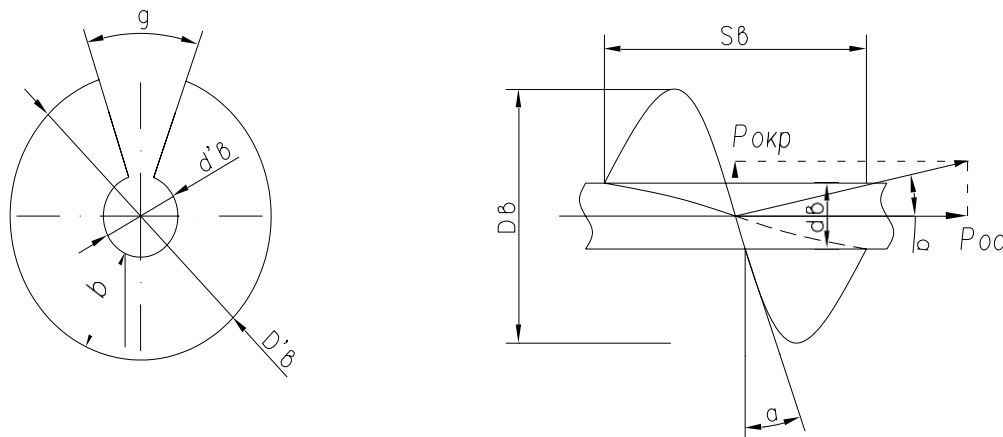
Схема до розрахунку розмірів заготовки шнека
